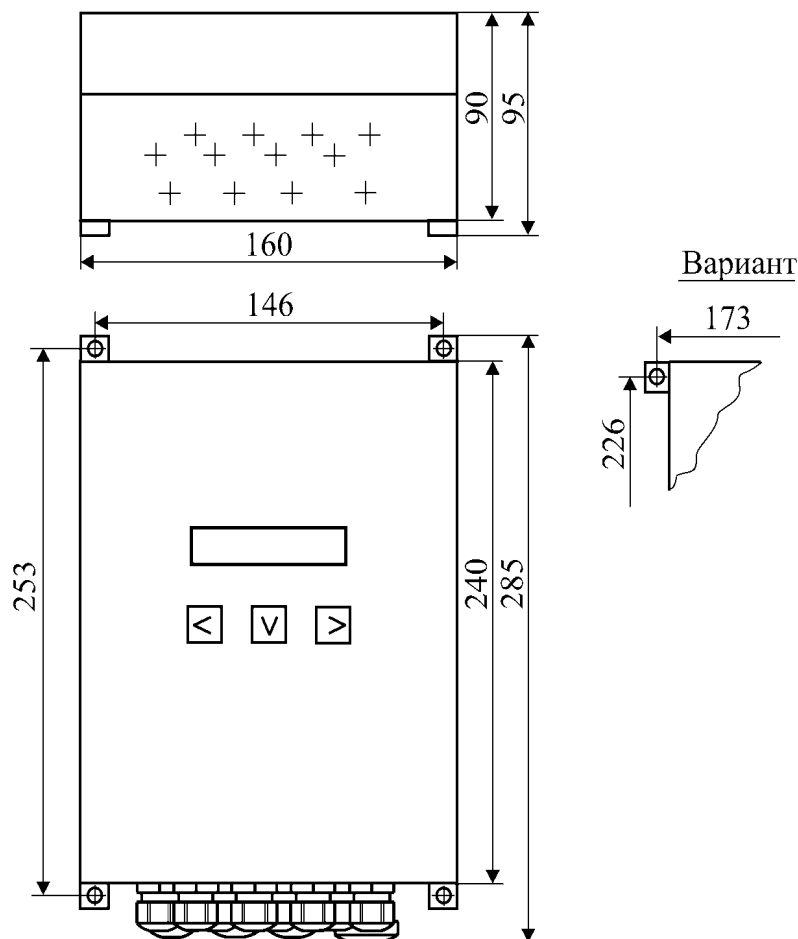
Габаритные, установочные и присоединительные размеры ПРЭ исполнений ЕК-6, ЕК-10, ЕК-15, ЕК-25 резьбового подсоединения
